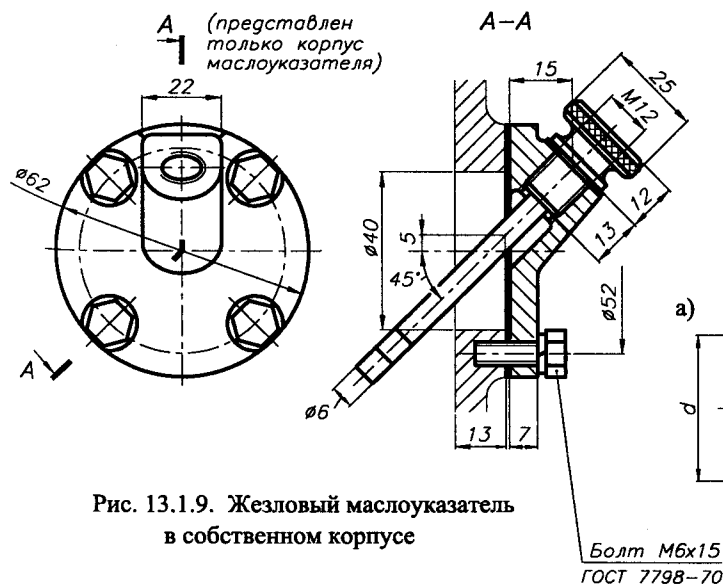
Жезловый маслоуказатель в собственном корпусе
